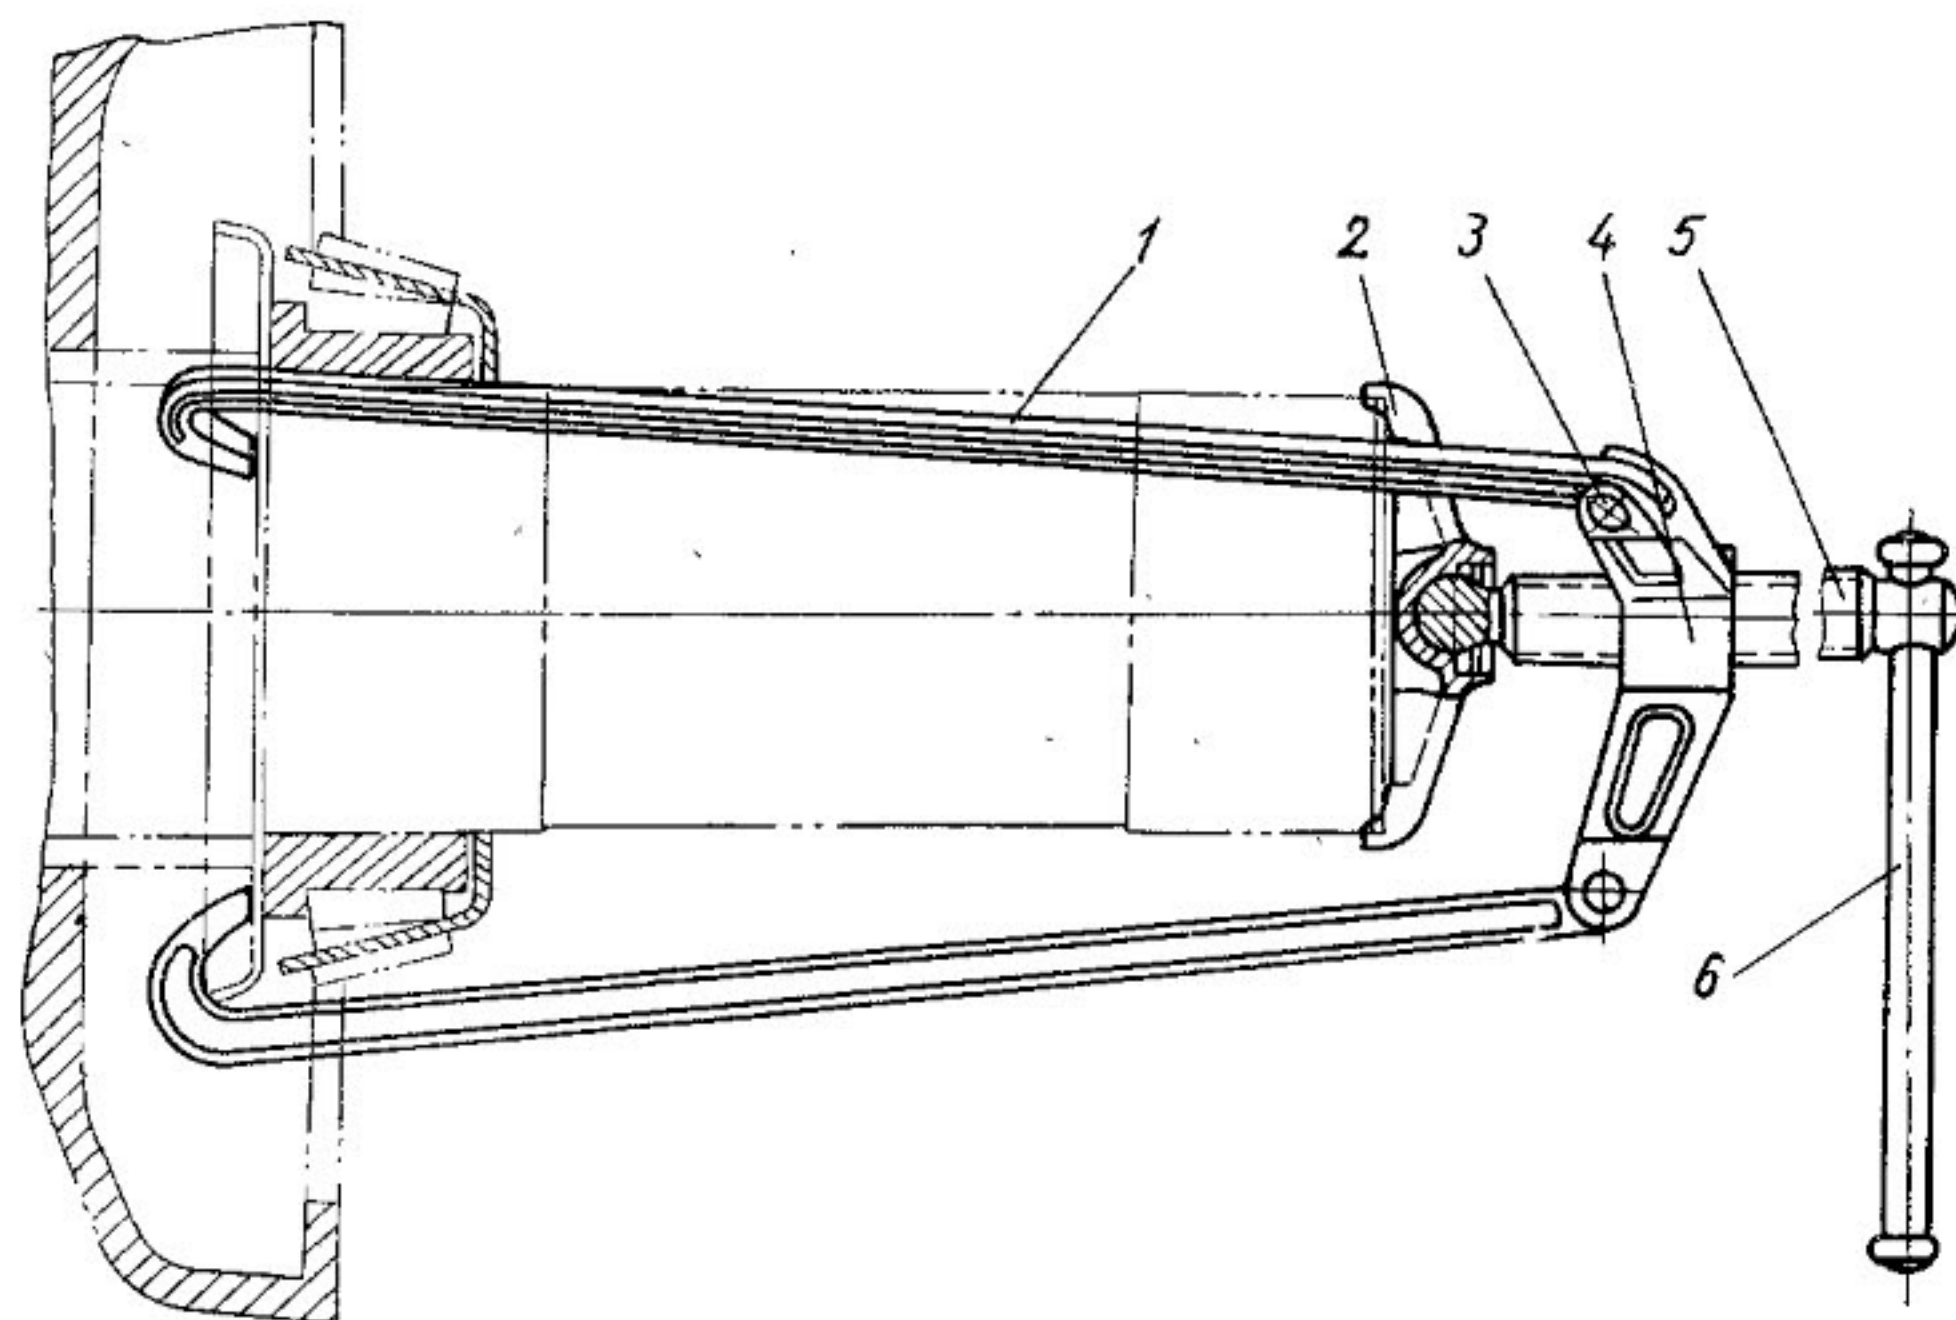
Съемник внутренних подшипников колес шасси: 1—крюк; 2—пята; 3—валик; 4—гайка; 5—винт; 6—вороток
